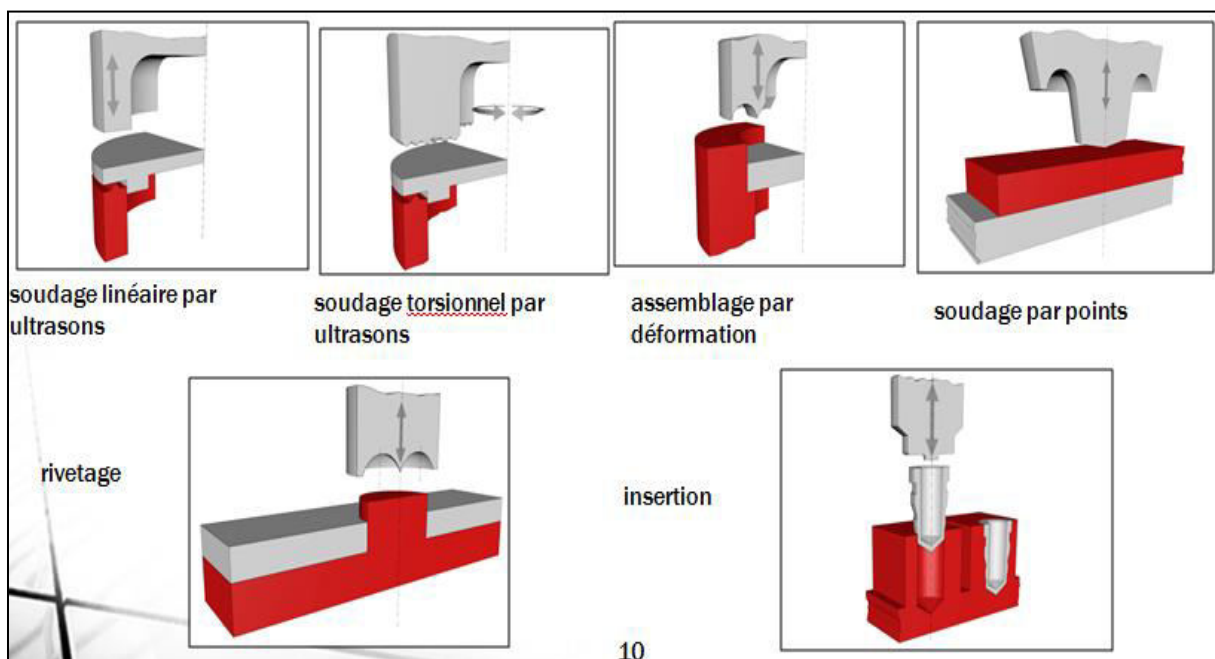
Assemblages possibles de soudure plastique par ultrasons
